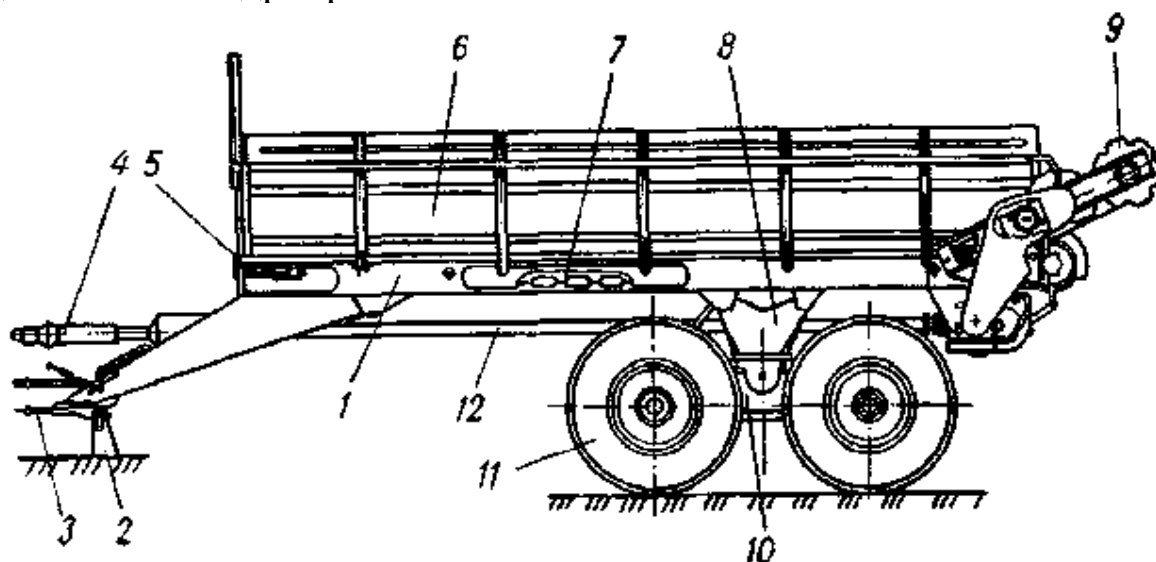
Разбрасыватель органических удобрений РОУ-6: 1 – рама; 2 – подставка; 3 – серьга; 4 – вал карданный; 5 – устройство натяжное; 6 – кузов; 7 – транспортер; 8 – кронштейн; 9 – устройство разбрасывающее; 10 – балансир; 11 – колесо ходовое; 12 – вал продольный
